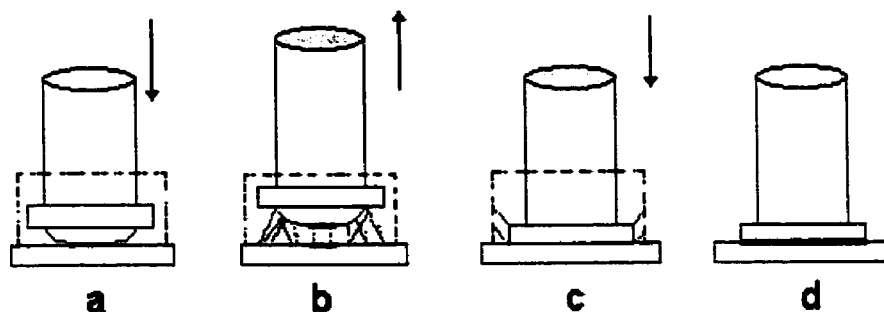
Séquences du soudage à l'arc de goujons au pistolet
